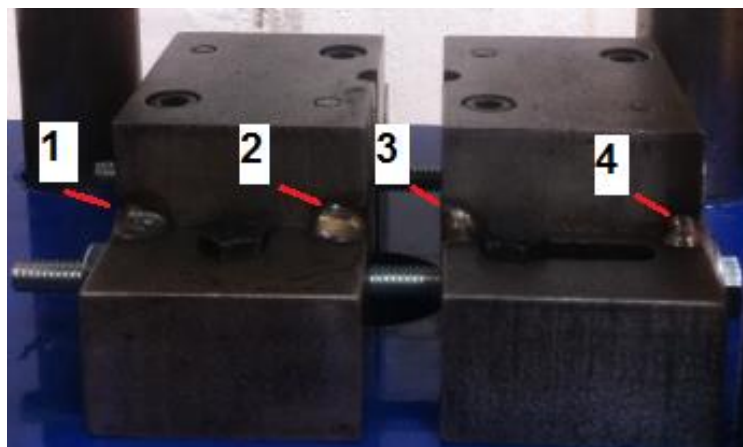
Puntos de soldadura para reforzar unión de las piezas.
